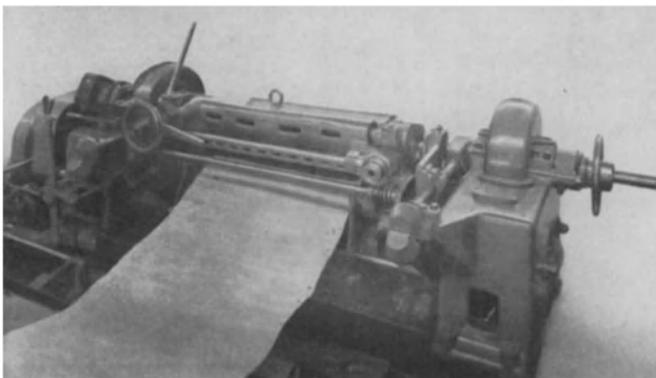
Schälmaschine mit auslaufendem Furnierband (RFR).
